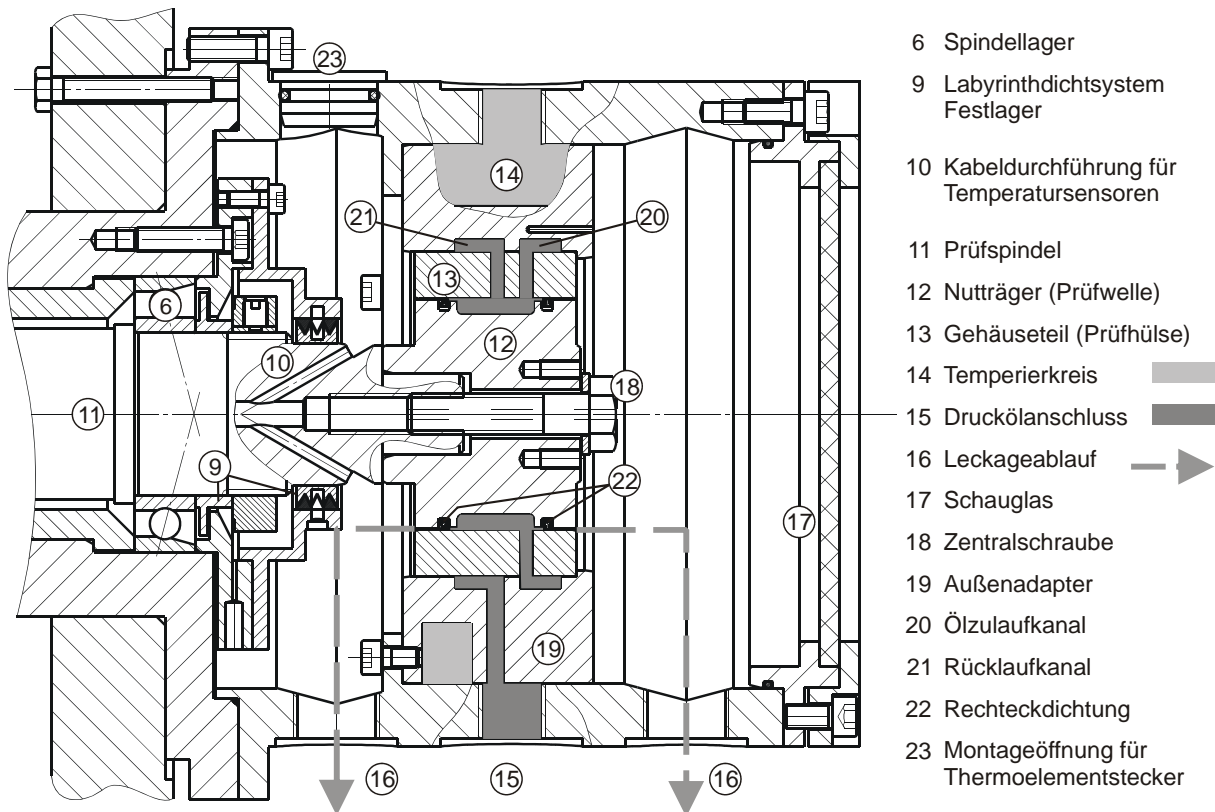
Detailansicht Prüfkopf mit rotierendem Innenteil
